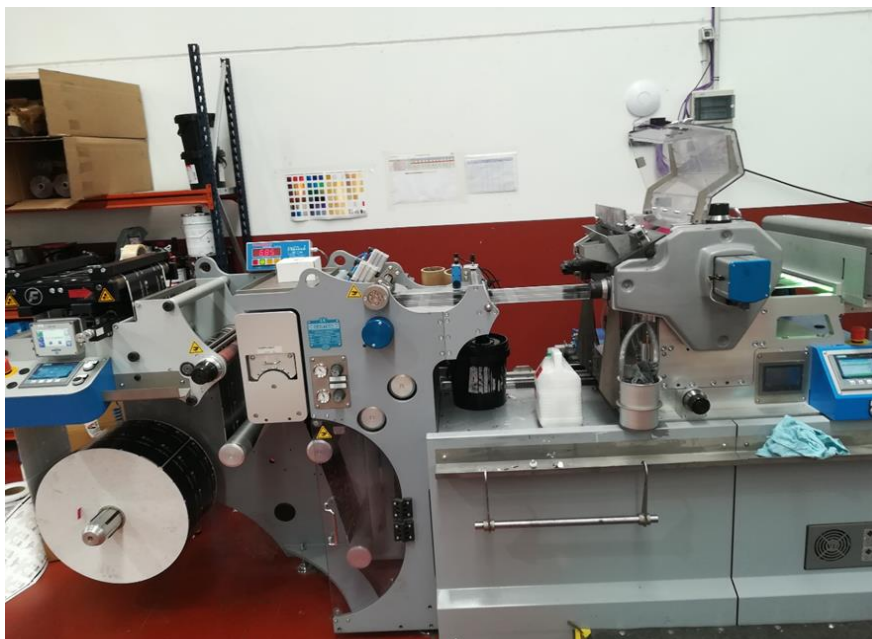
Desbobinado integrado con unidad de barnizado. Fuente: Fotografía del autor.
